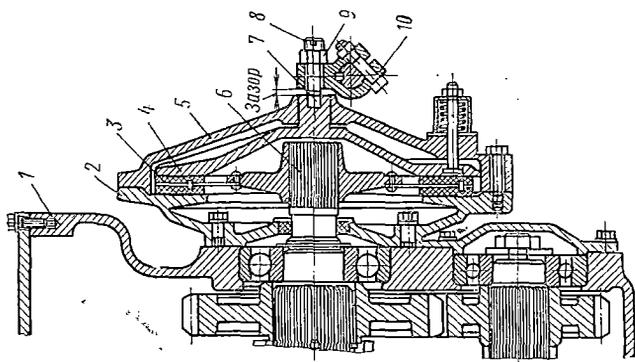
Ручной тормоз самоходного грейдера ДЗ-31А:
